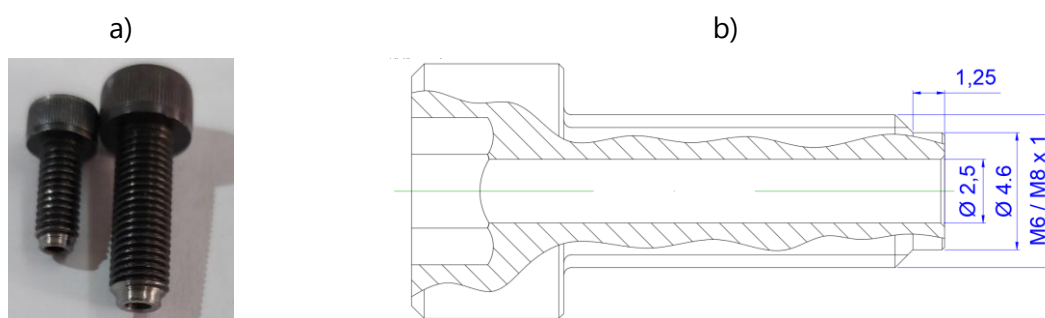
a) Parafusos de fixação, b) desenho esquemático.
